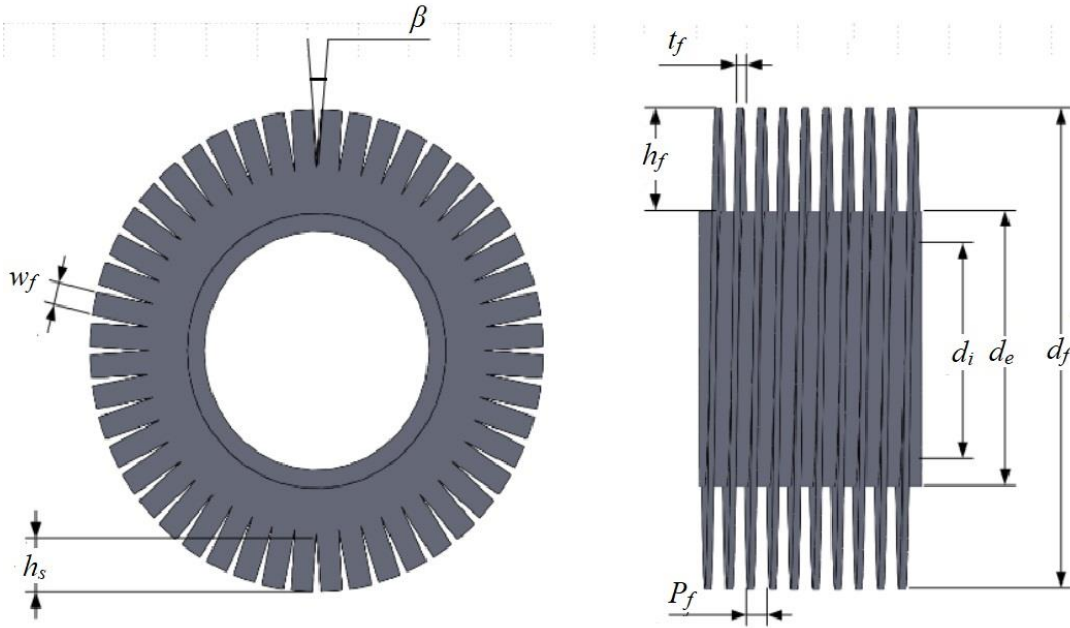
Parámetros para las geometrías de aletas empleadas
